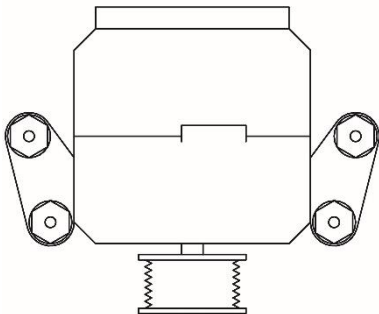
Montaggio dell'alternatore - montaggio su slitta vista anteriore
